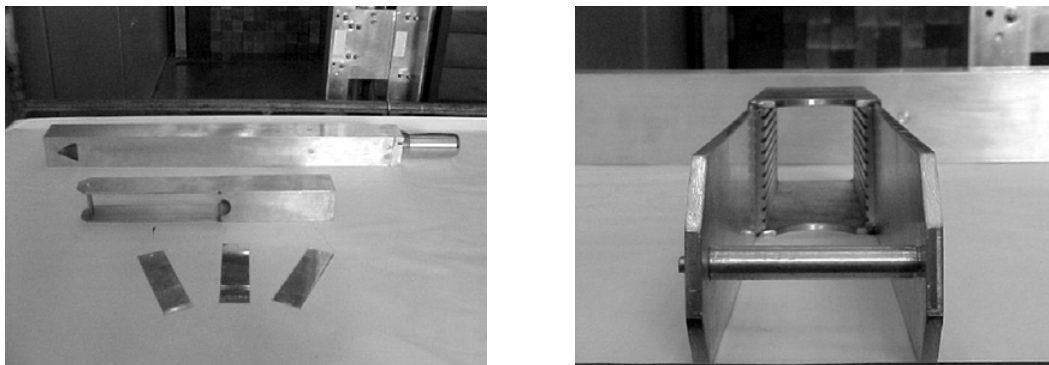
Componentes do sistema de irradiação. À esquerda, elemento de irradiação, suporte e miniplacas. À direita, detalhe do suporte com capacidade de posicionar 10 miniplacas para irradiação.
